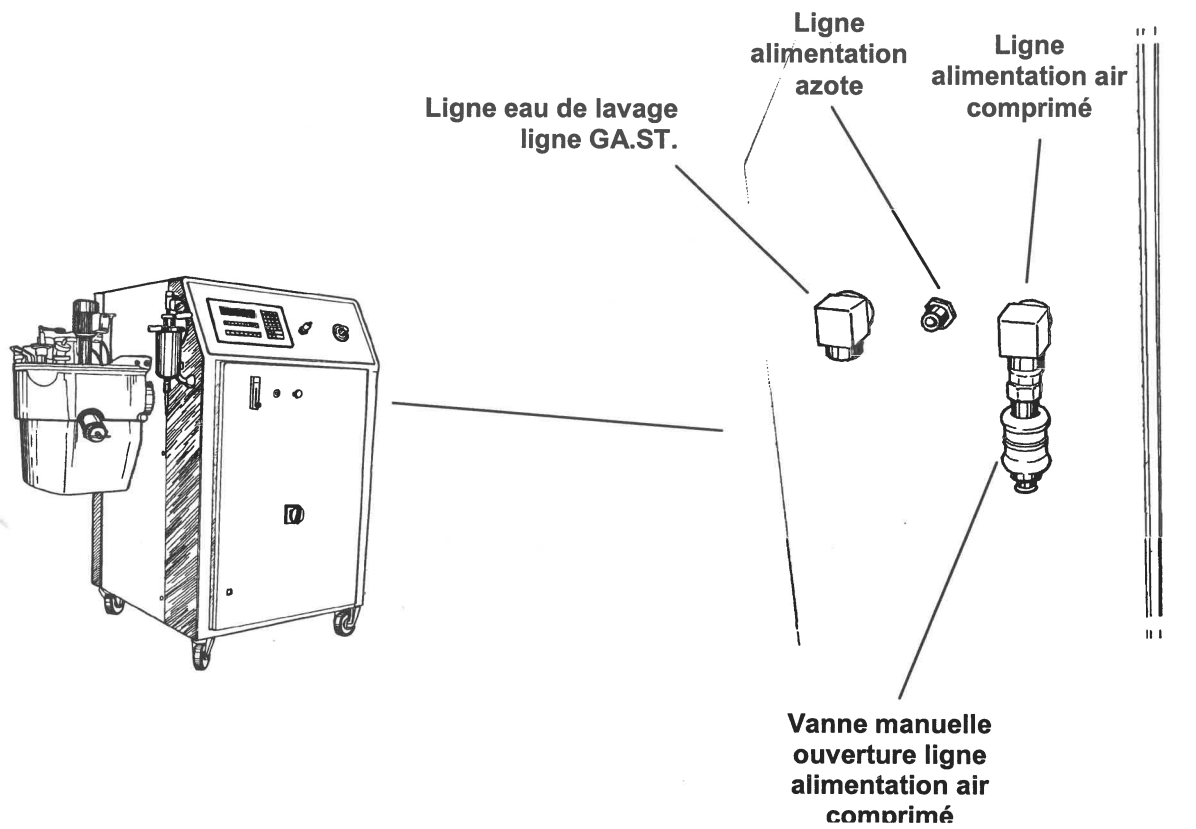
Dispositifs sur l'arrière de la machine est connexions aux services
